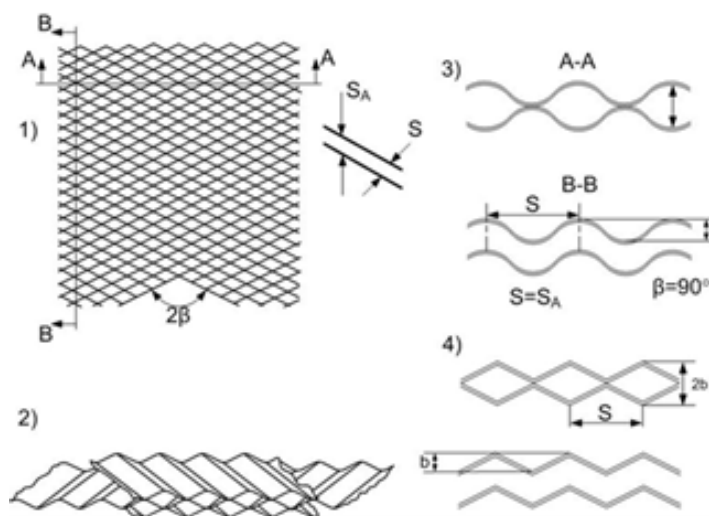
Схема гофрированного поля пластин и образуемых ими каналов: 1, 2 – пересечение гофр двух смежных пластин; 3, 4 – поперечное сечение каналов с различной формой гофрировки
